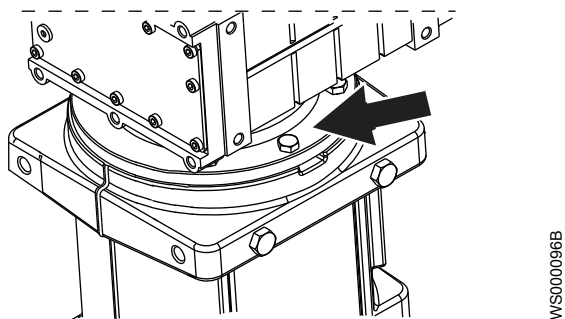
SY 4860: Винты крепления двигателя к подставке
